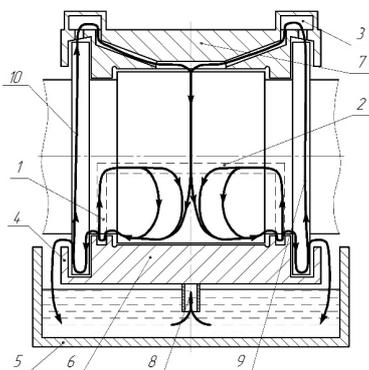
Смазочный слой с внутренней циркуляцией: 1 - торцевые канавки; 2 - продольная канавка; 3 - верхний накопитель масла; 4 - малый картер; 5 - картер; 6 - нижний вкладыш; 7 - верхний вкладыш; 8 - подсос смазки в слой; 9 - движение масла из смазочного слоя в торцевые канавки, в продольную канавку и в смазочный слой; 10 - движение масла из малого картера на смазку упорной части, в верхний накопитель масла и в смазочный слой
